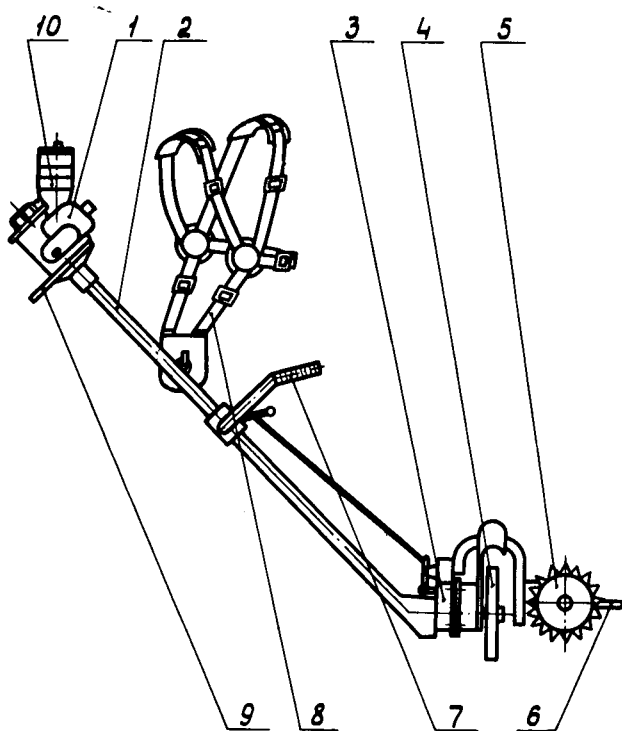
Общий вид конструкции ручного грунтометра
